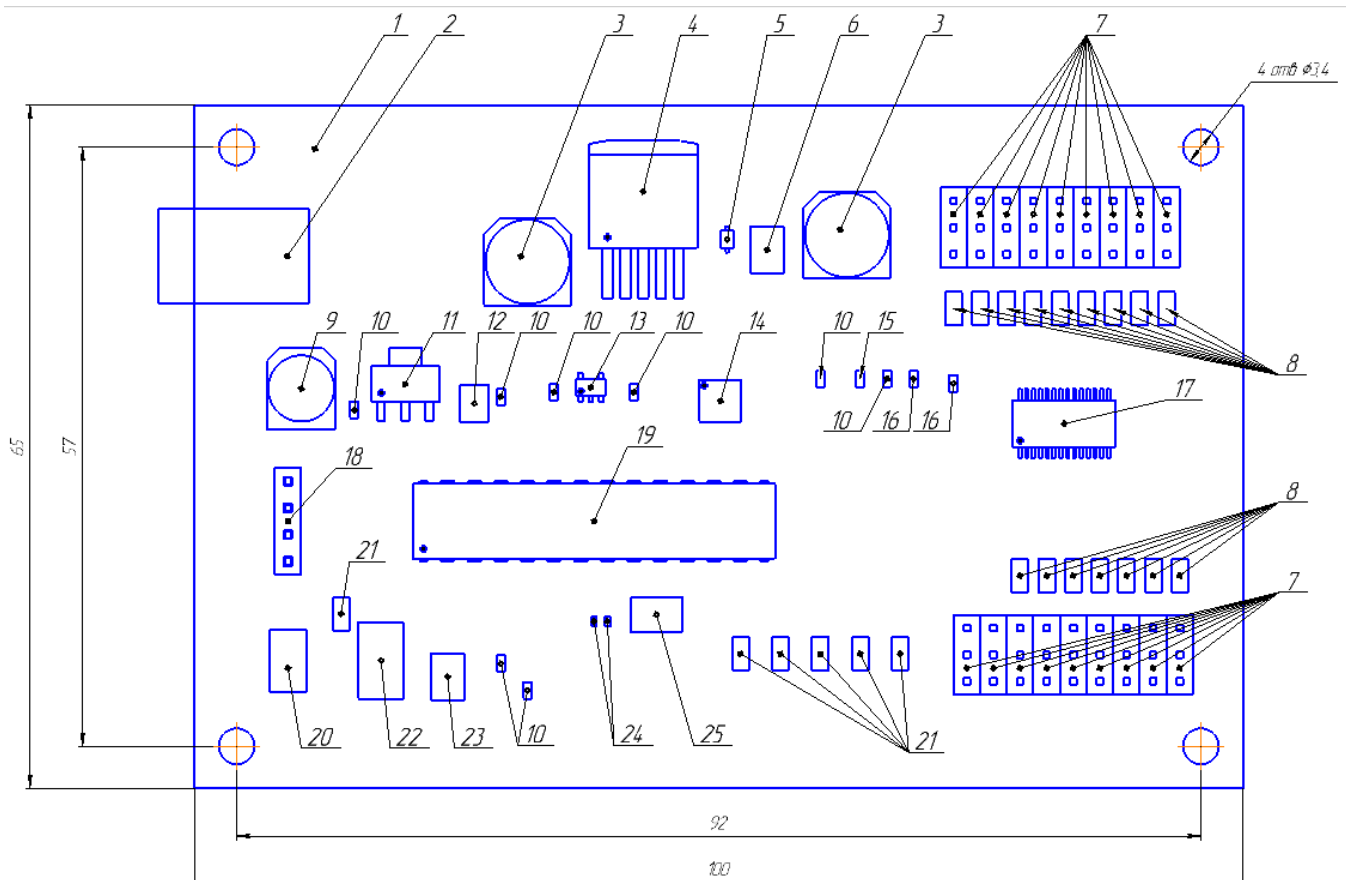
Разработка сборочного чертежа в САПР Компас 3D
